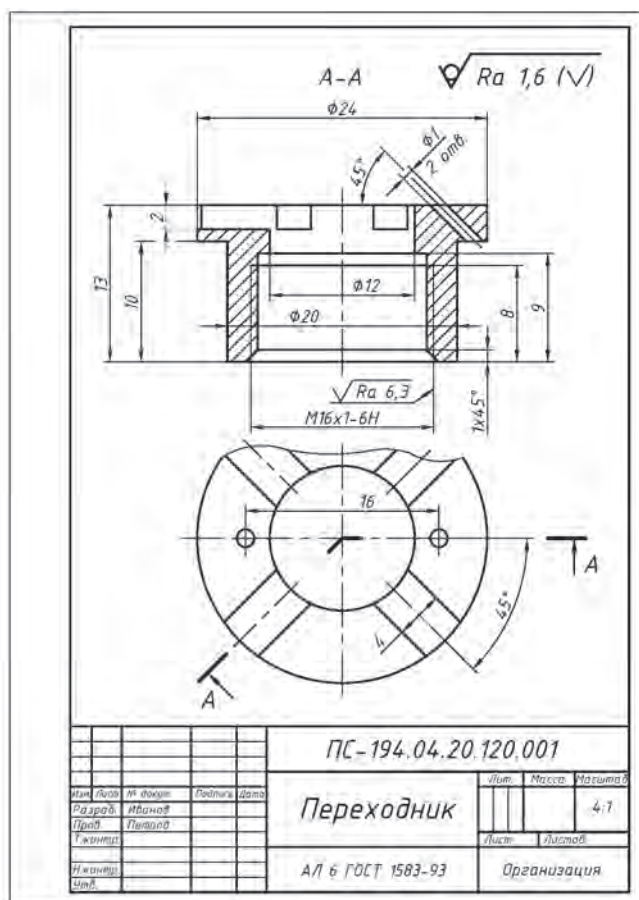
Чертеж детали «Переходник», выполненный в AutoCAD
